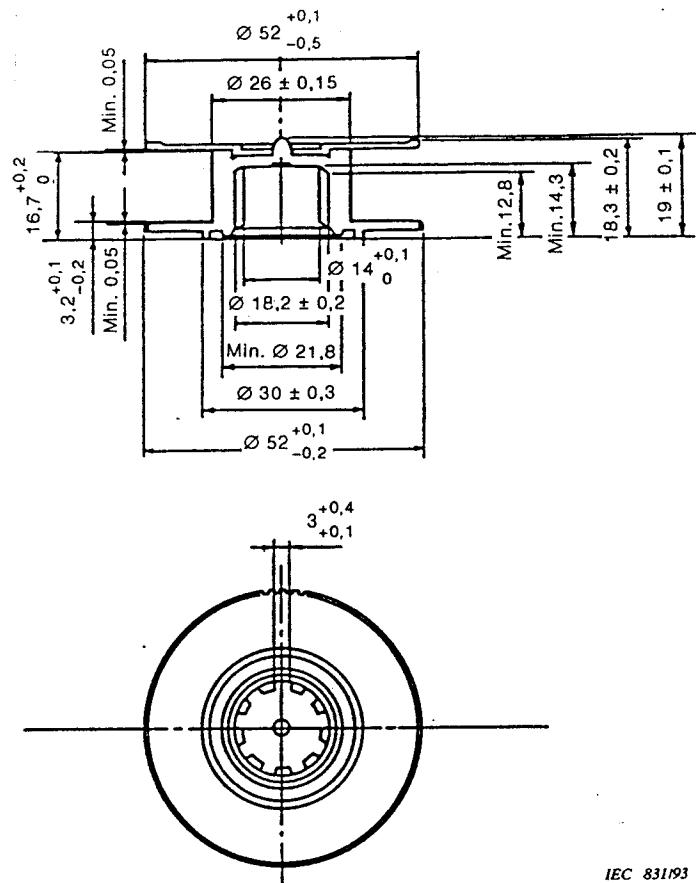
Dimensions de la bobine débitrice de la cassette de petite dimension
